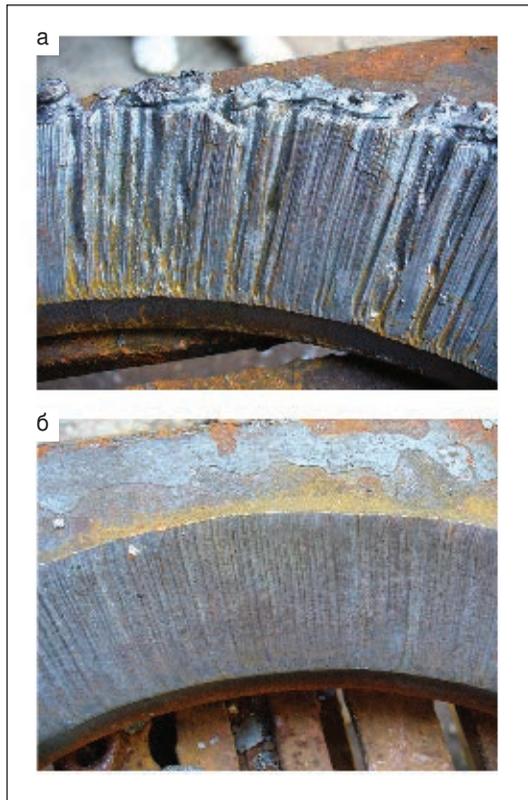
Качество реза фасок: а — ручным резакром; б — с использованием приспособления. Заготовки перевернуты
